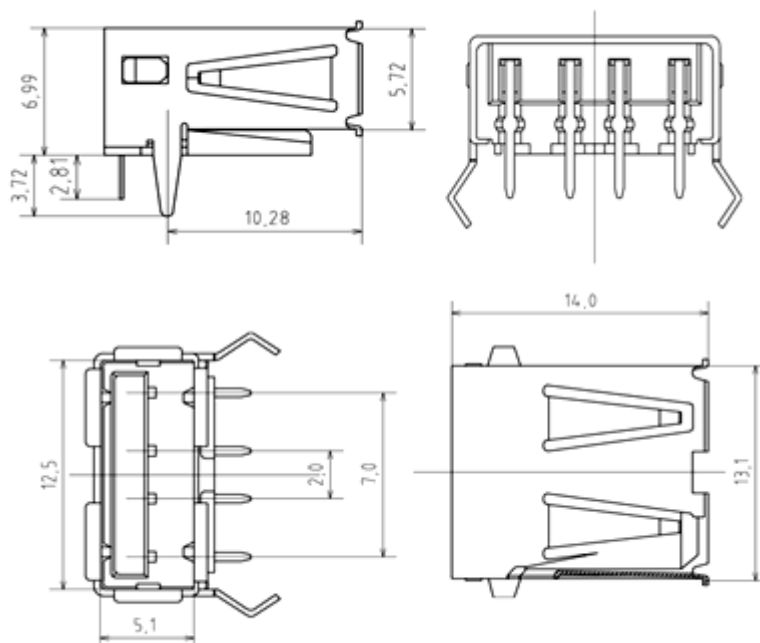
Цоколевка и размеры разъема USB type A
